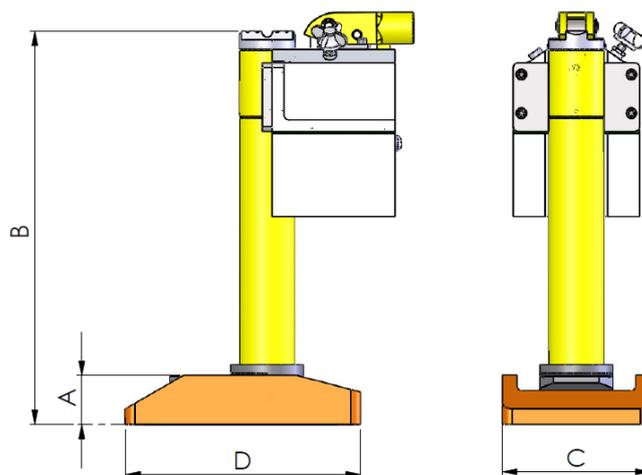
Dimensões do Macaco Hidráulico TMU1010 Fechado
